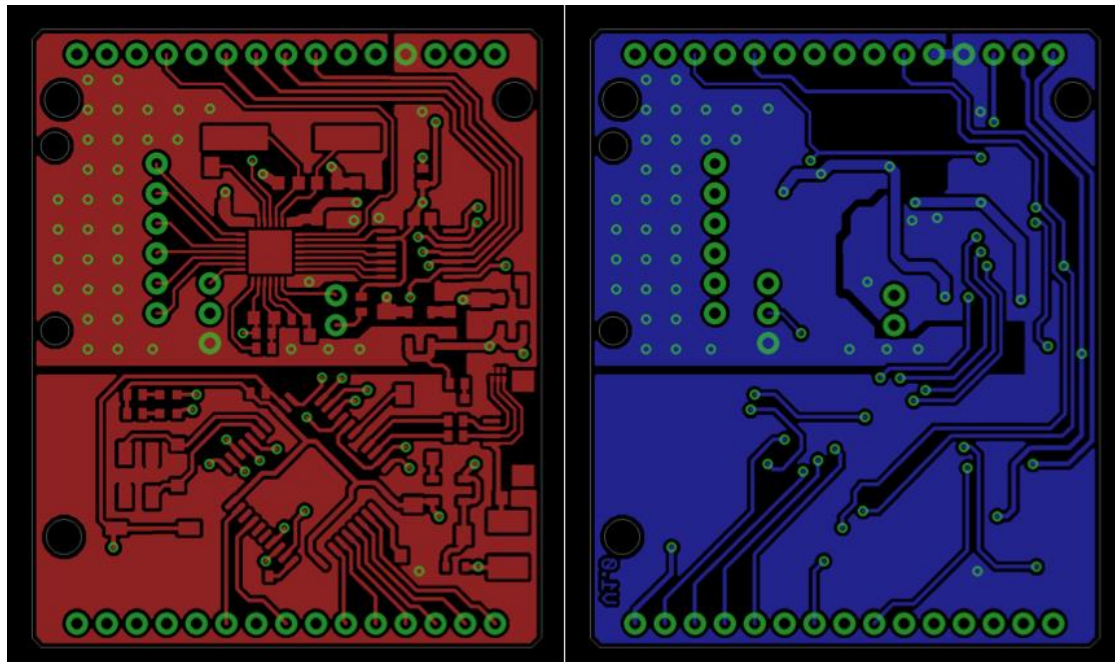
Capa superior (izquierda) y capa inferior (derecha) del circuito impreso
